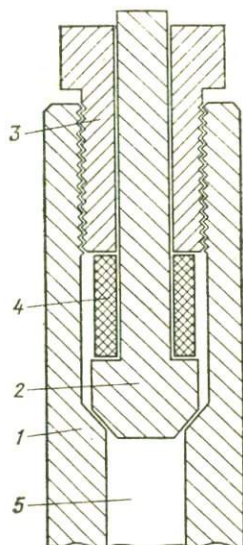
Беспрокладочный затвор для титановых автоклавов конструкции ИЭМ АН СССР: 1 — титановый корпус автоклава, 2 — титановый обтюратор, 3 — нажимная гайка, 4 — кольцо из сплава на основе никеля, 5 — рабочий объем автоклава
